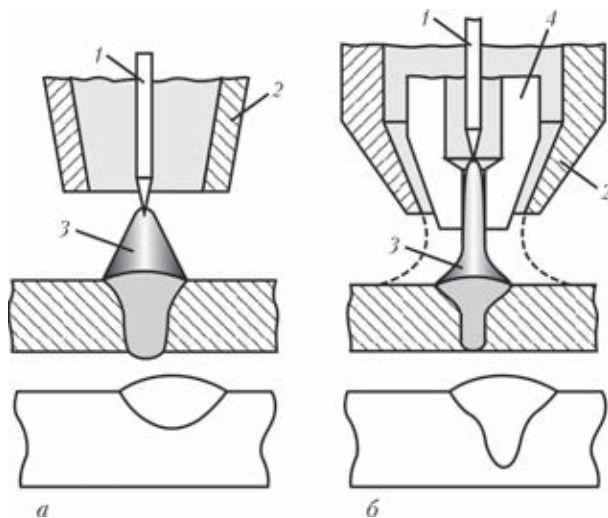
Схема процесса и форма проплавления сварного шва при дуговой (а) и плазменно-дуговой (б) сварке неплавящимся электродом: 1 — вольфрамовый электрод; 2 — сопло защитного газа; 3 — сварочная дуга; 4 — плазмообразующее сопло
